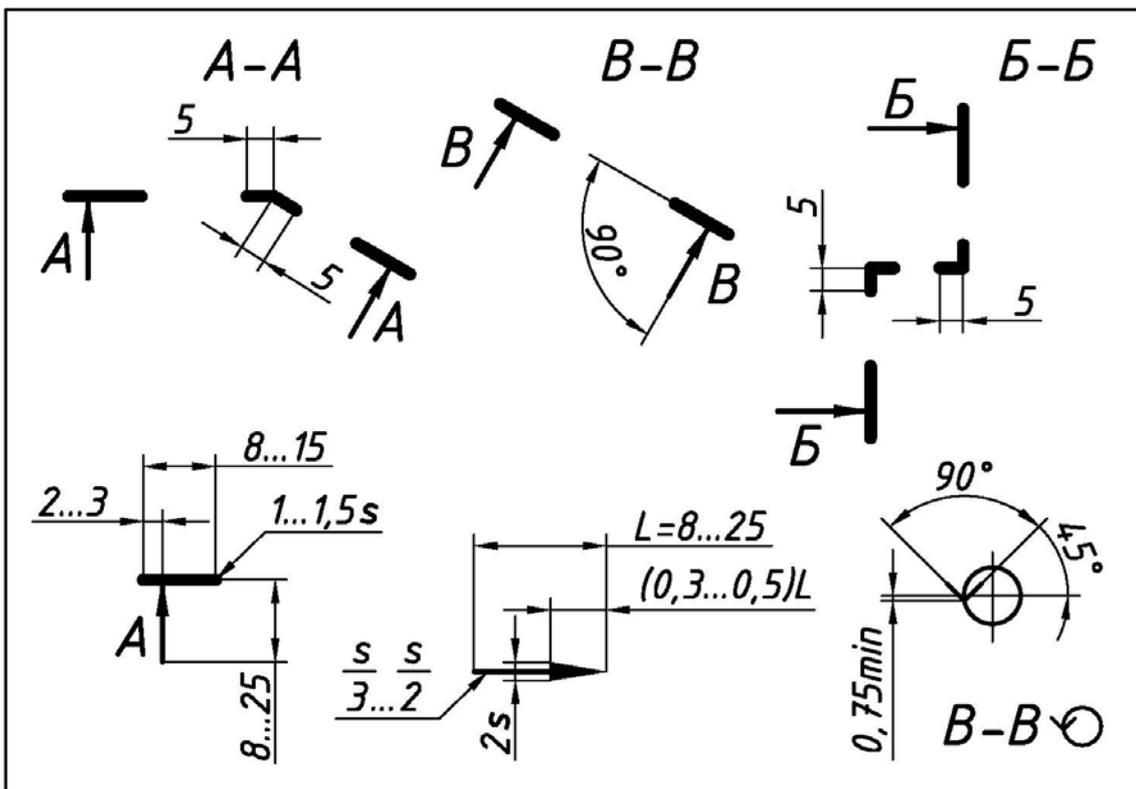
Элементы для обозначения разрезов, сечений и их основные размеры
